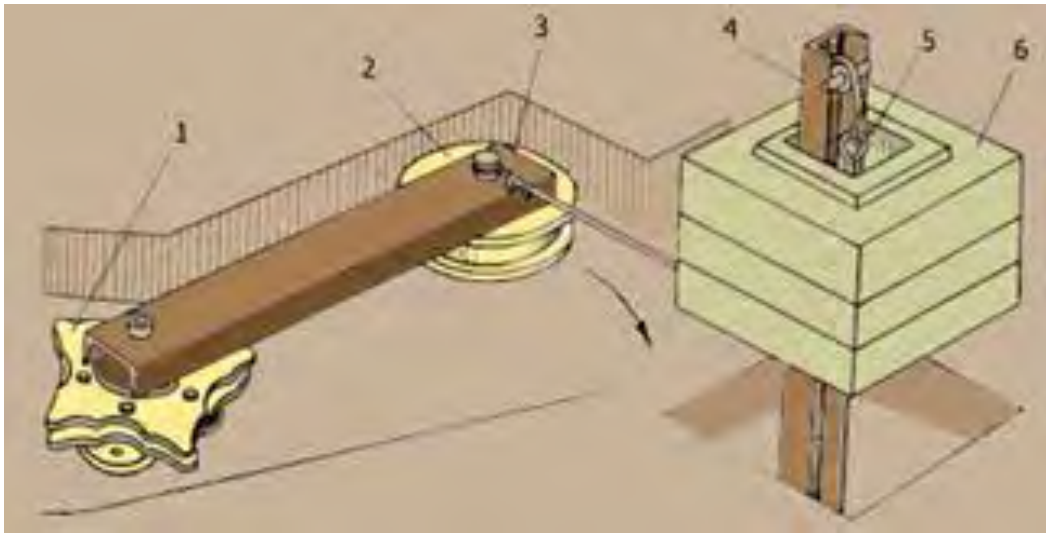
Автоматичний натяжний пристрій конвеєра КСГ-7:
